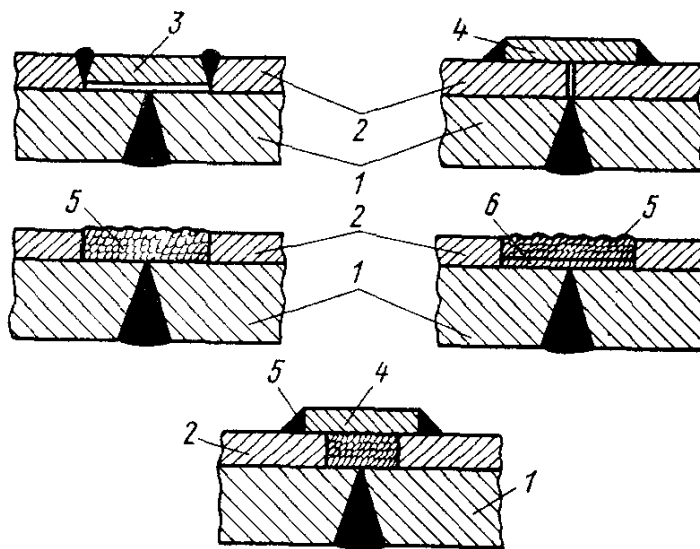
Варианты конструктивного оформления соединения при сварке биметалла медь—сталь; 1 — стальной слой, 2 — медный слой; 3 — проставка, 4 — накладка, 5 — наплавка; 6 — подслой
